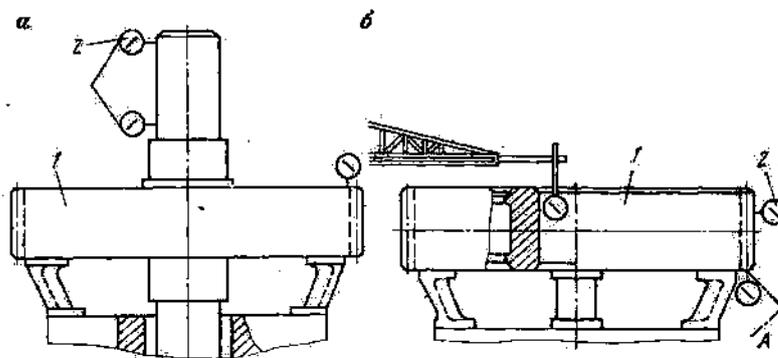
Выверка положения заготовки при установке на зубофрезерном станке.
